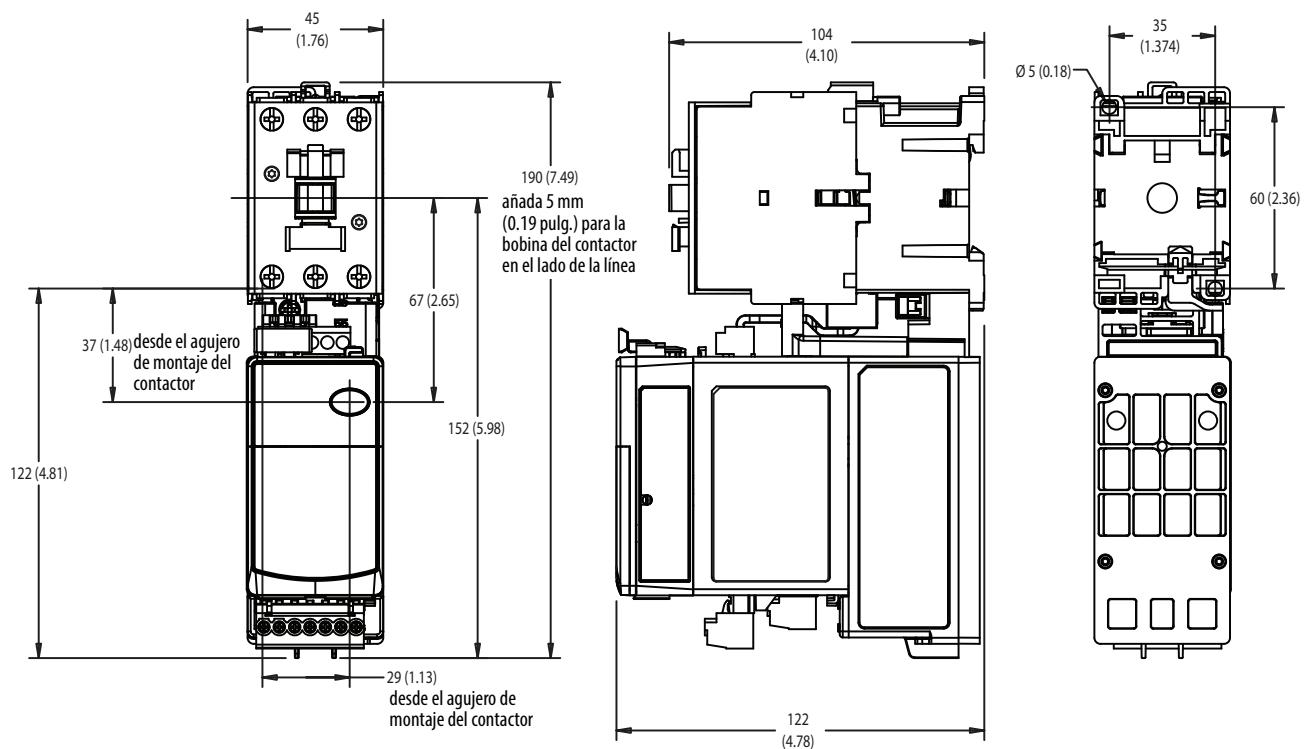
Relé de sobrecarga E300/E200 montado en un contactor Boletín 100-C43...-C55
